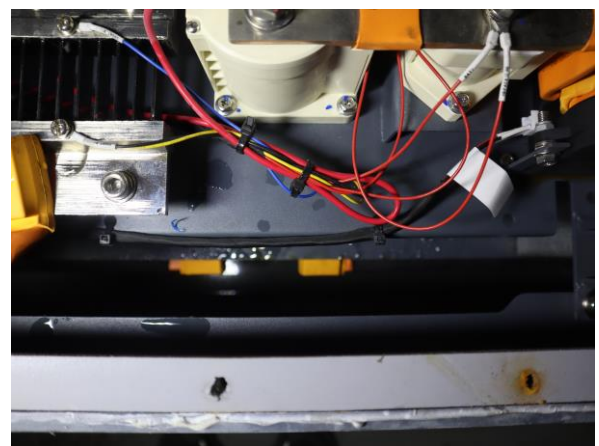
试验后进尘检查(After test,ingress of dust inspection)
